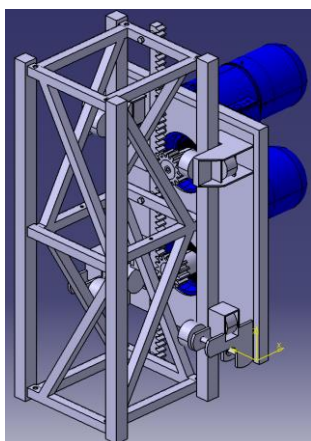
Engrane del grupo motor con los mástiles. Vista 3D
